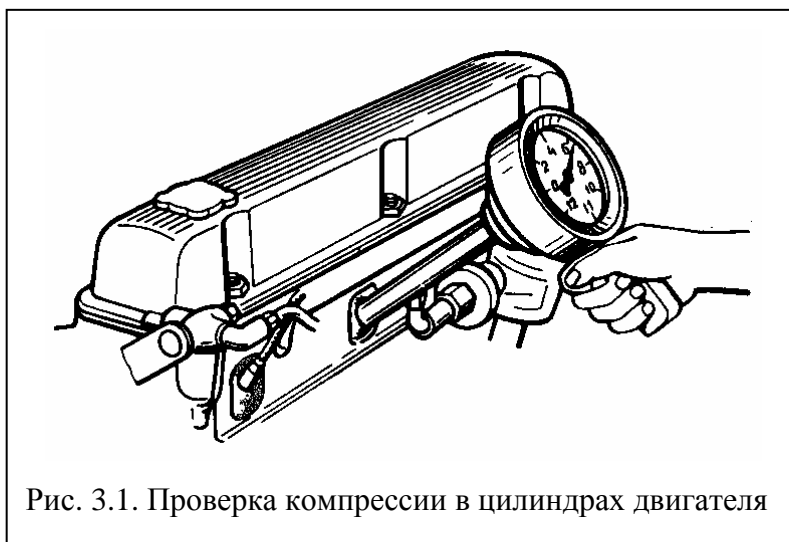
Проверка компрессии в цилиндрах двигателя
